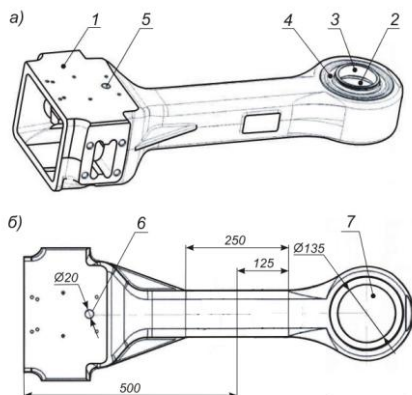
Корпус сцепки со сферическим подшипником:
